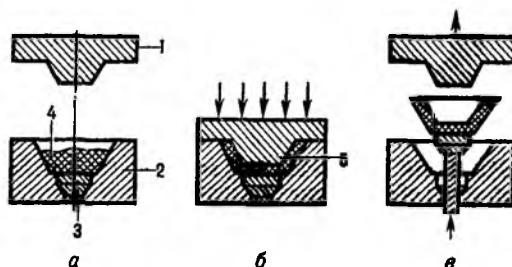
Изготовление изделий прессованием: а — загрузка прессматериала в нагретую прессформу; б — прессование; в — выталкивание изделия; 1 — пуансон; 2 — матрица; 3 — выталкиватель; 4 — прессматериал; 5 — готовое изделие.
